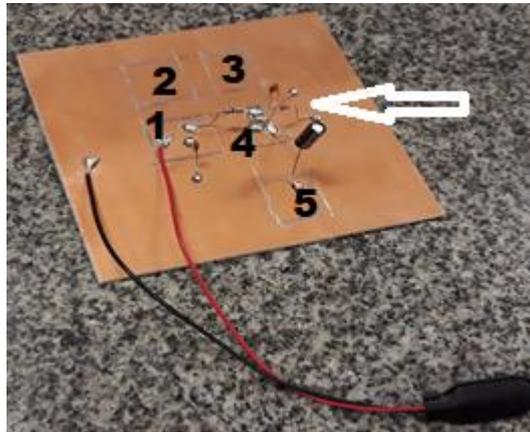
Soldagem do capacitor polarizado de $1\mu F$
